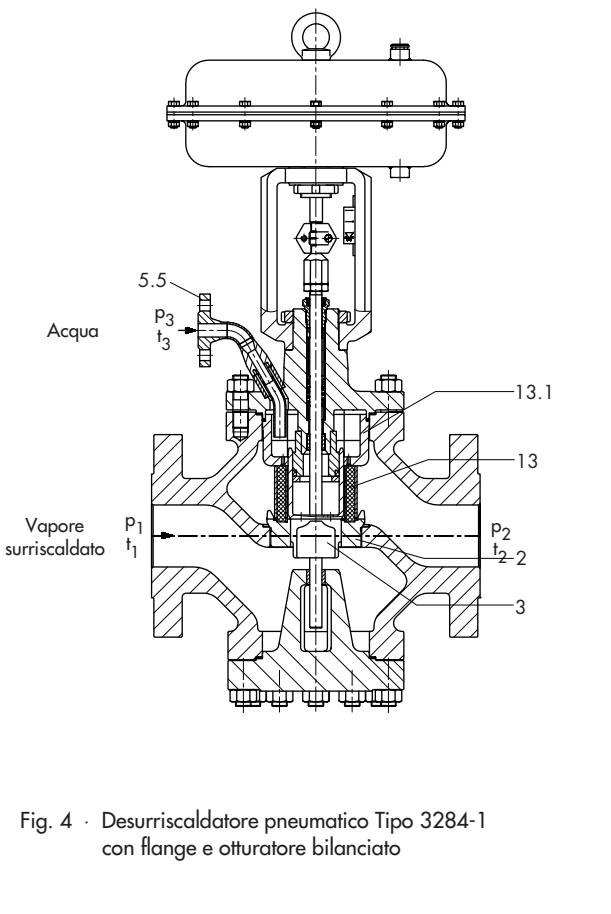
· Desurriscaldatore pneumatico Tipo 3284-1 con flange e otturatore bilanciato
